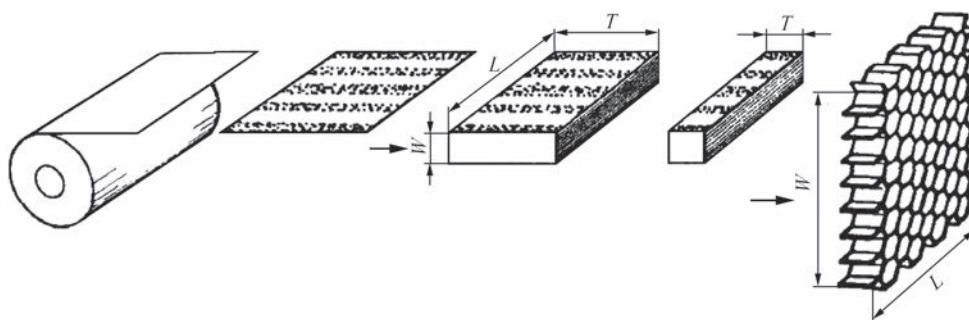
Процесс изготовления сотового наполнителя методом растяжения пакета [3]
